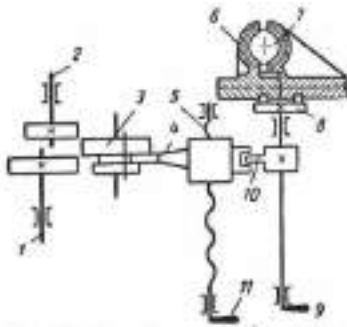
Схеми блокувального пристрою: 1, 2 — вал; 3 — зубчасте колесо; 4 — маткова гайка; 5 — гвинт; 6 — гайка; 7 — ходовий гвинт; 8 — диск; 9, 11 — руків'я; 10 — язичок
